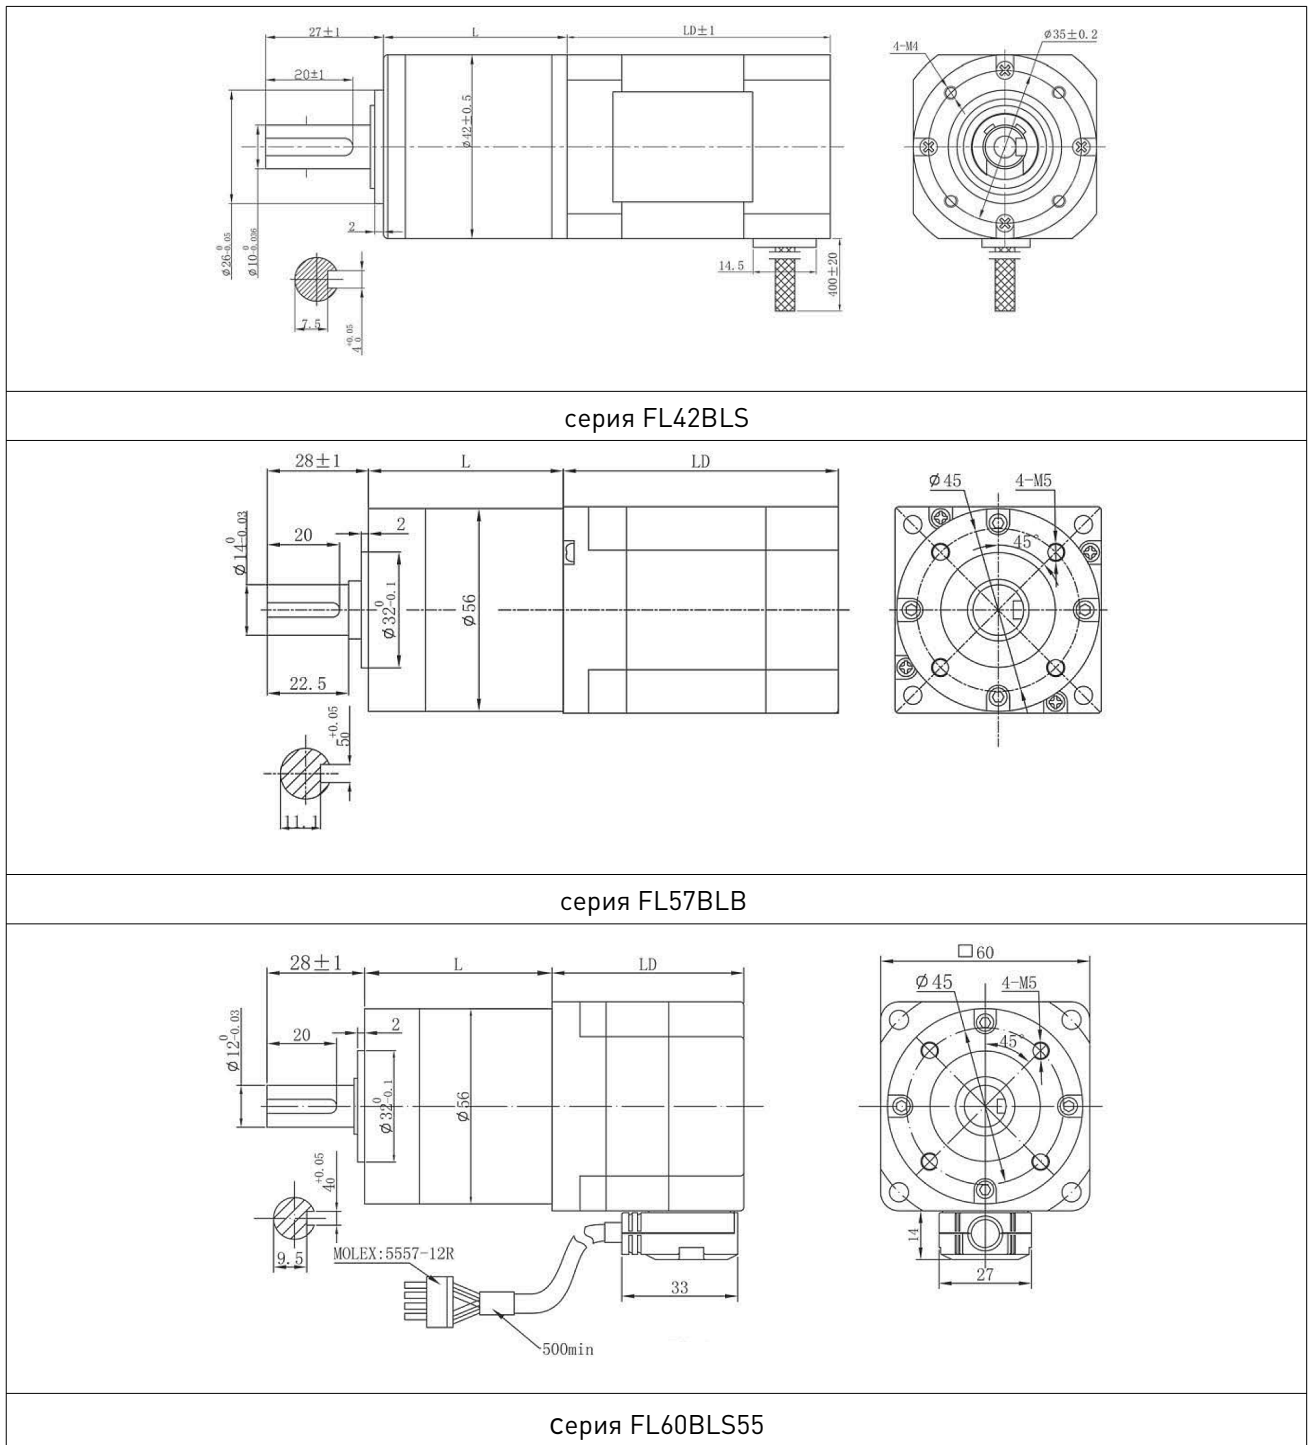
Габаритные и установочные размеры мотор-редукторов
